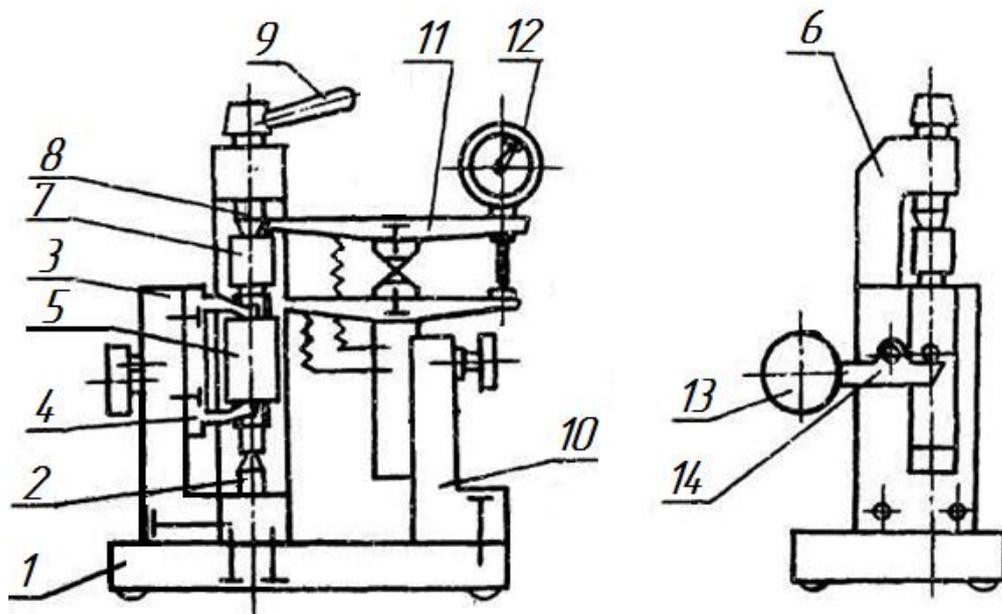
Прибор для контроля осевого зазора винтовой пары
